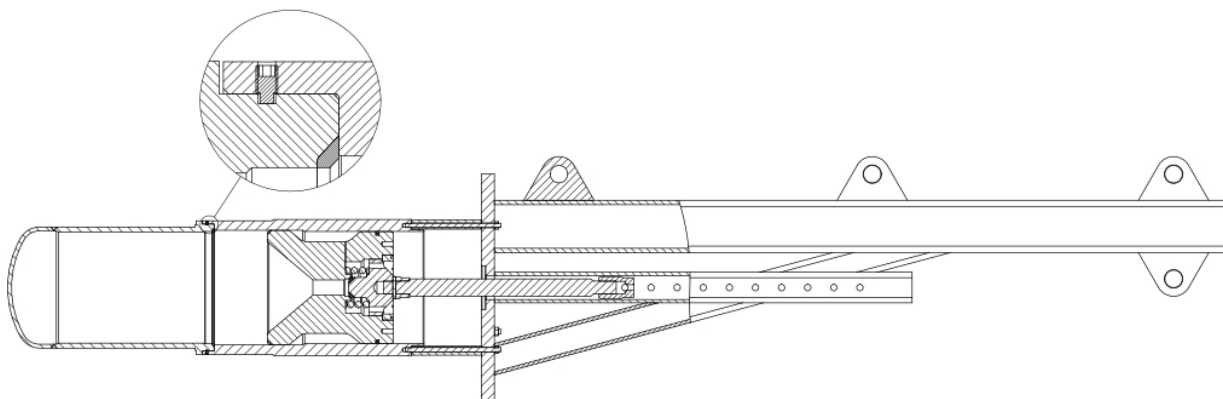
Ensemble de pièces internes monté sur le TID - Type cartouche
